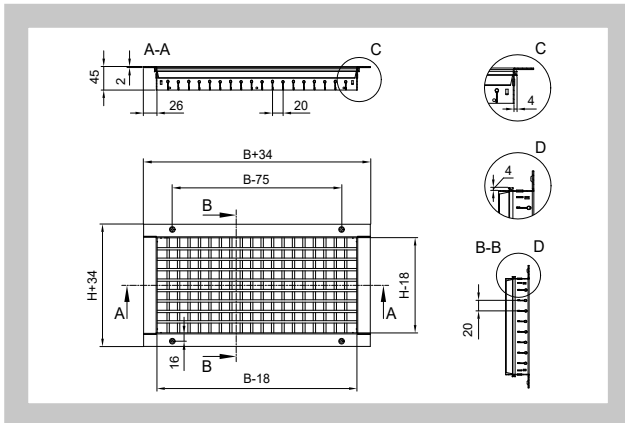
Einstellbare Lamellen horizontal - zweireihig B > 750 mm
